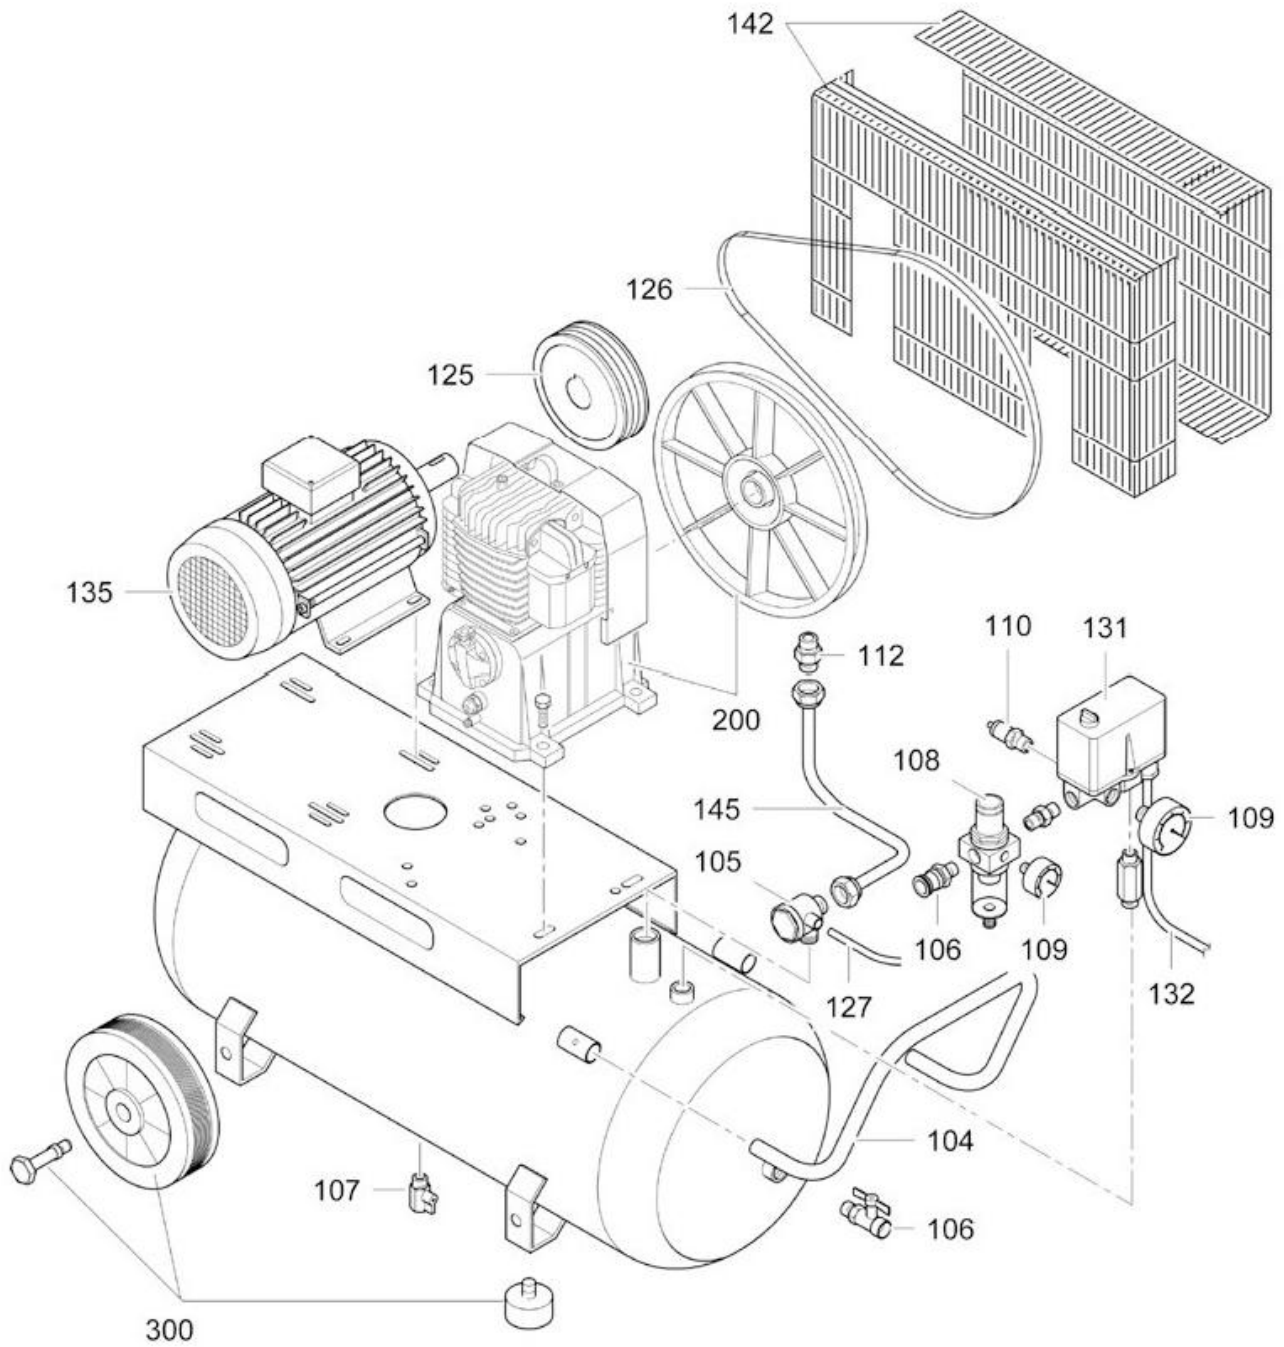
Náhradní díl 1 – AIRSTAR 603/50
